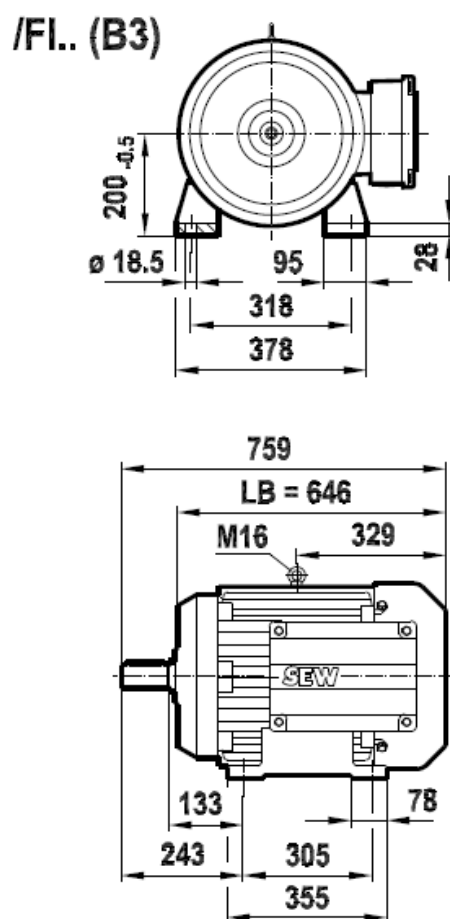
Desenho técnico do motor elétrico DRN200L.
